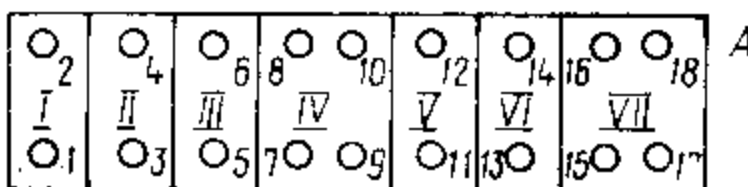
Порядковые номера гаек и шпилек коренных подшипников:
